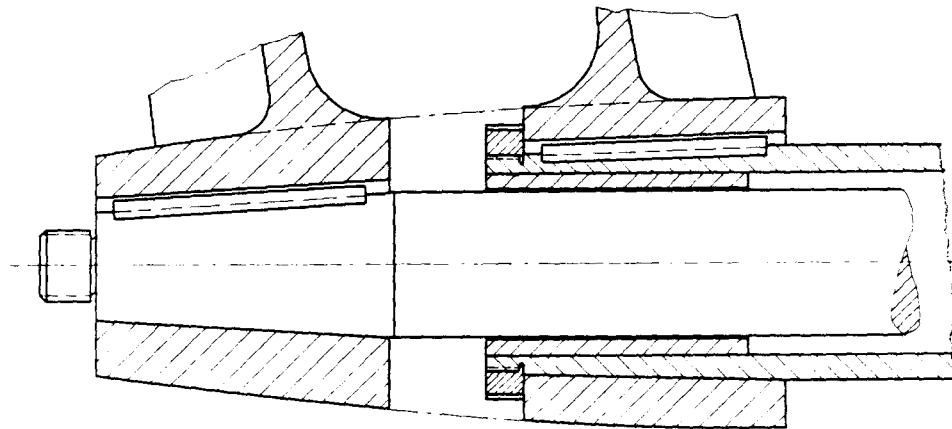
Befestigung von gegenläufigen Propellern; beide Propeller mittels Konussitz und Paßfeder befestigt
